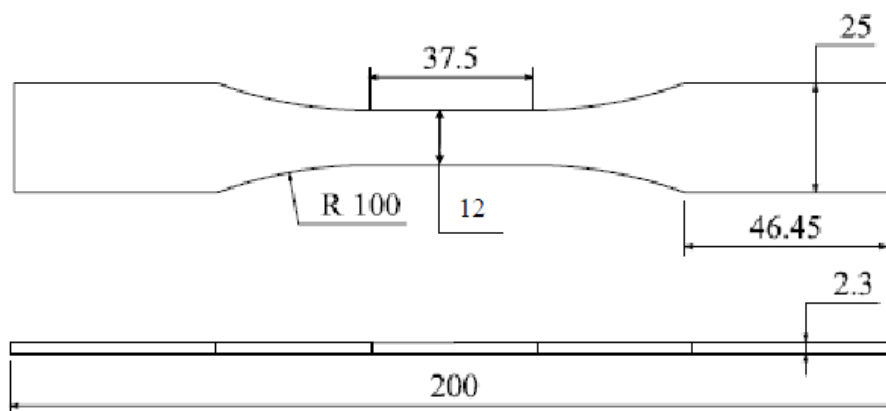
Géométrie des échantillons de fatigue (dimensions en mm).
